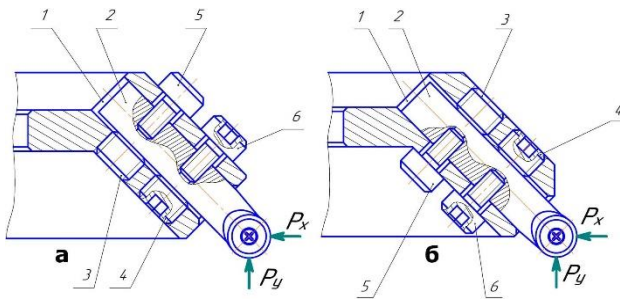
Два варіанти (а, б) встановлення циліндричної різальної вставки в корпусі торцевої фрези
